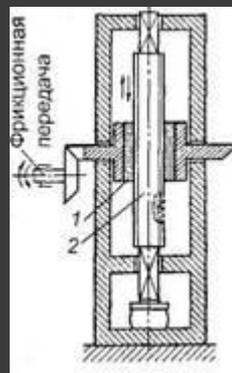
Передача винт-гайка: 1 — гайка; 2 — винт
